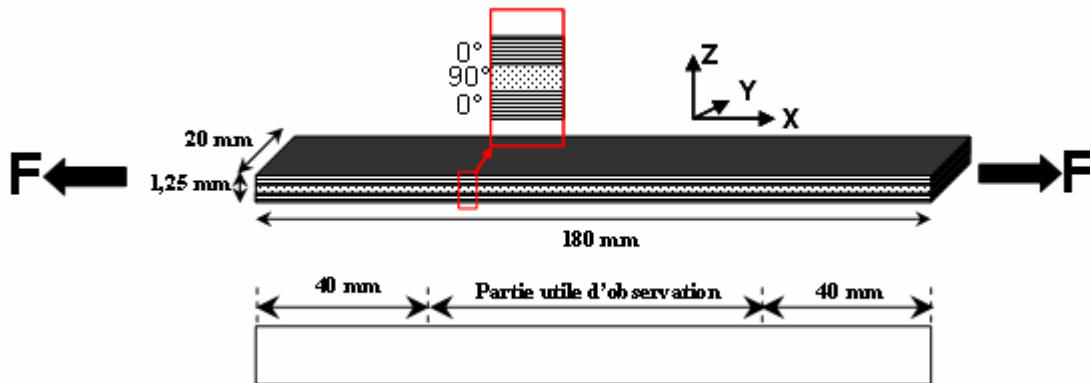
Géométrie et dimensions des éprouvettes [0/90₃/0] de carbone/époxyde IM7/977-2.
